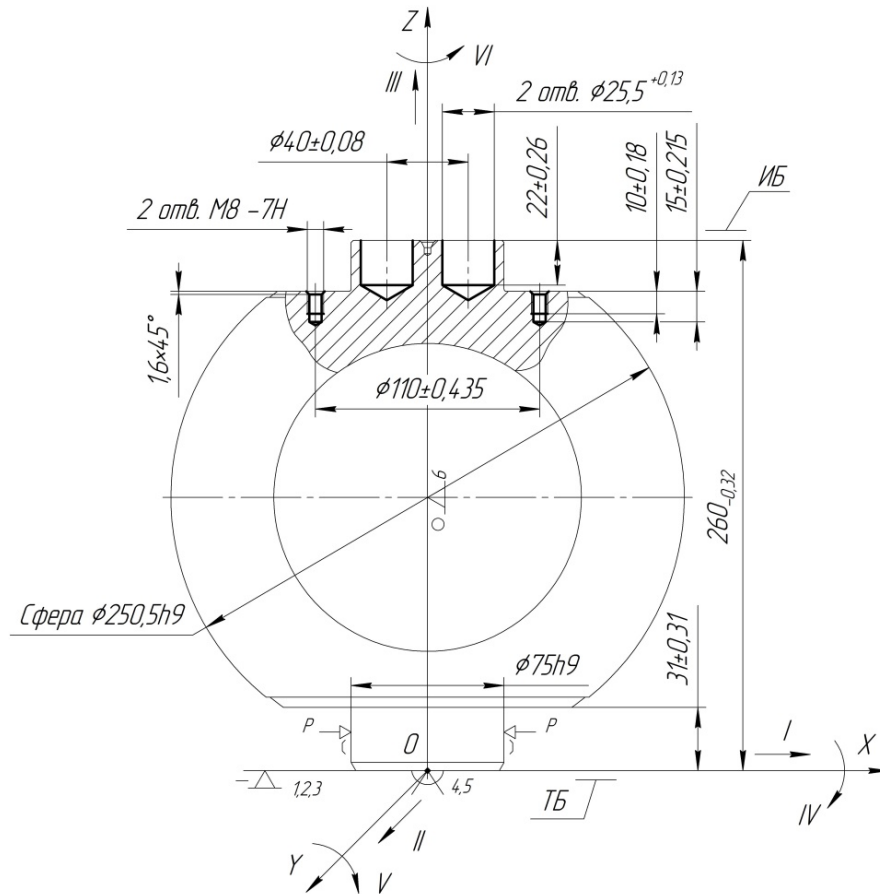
Базування заготовки на операції 050. Схема №2
